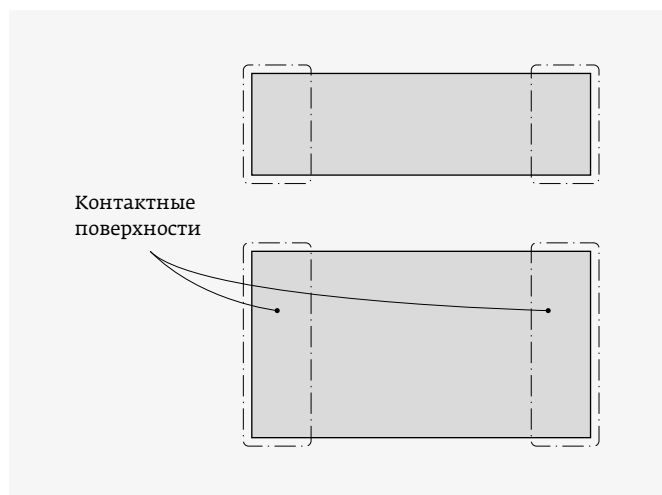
Эскиз общего вида конденсатора серии K10-90
